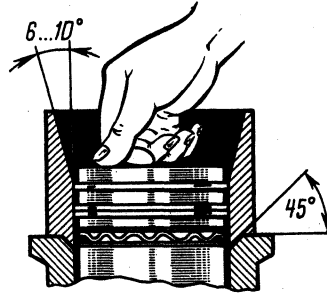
Приспособление для сжатия поршневых колец двигателя
